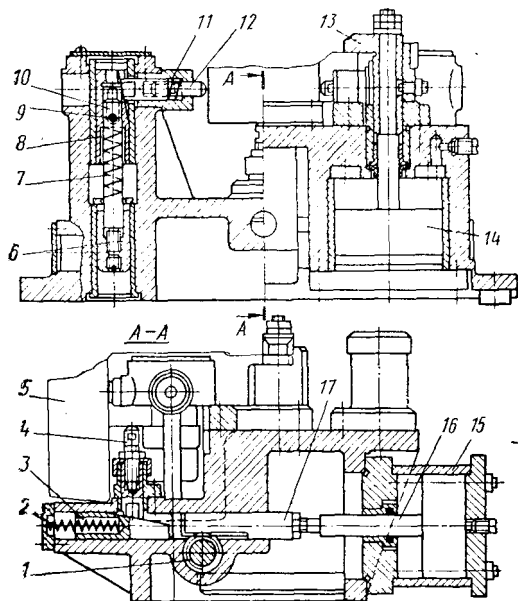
Фрезерное приспособление с элементами внутренней механизации
